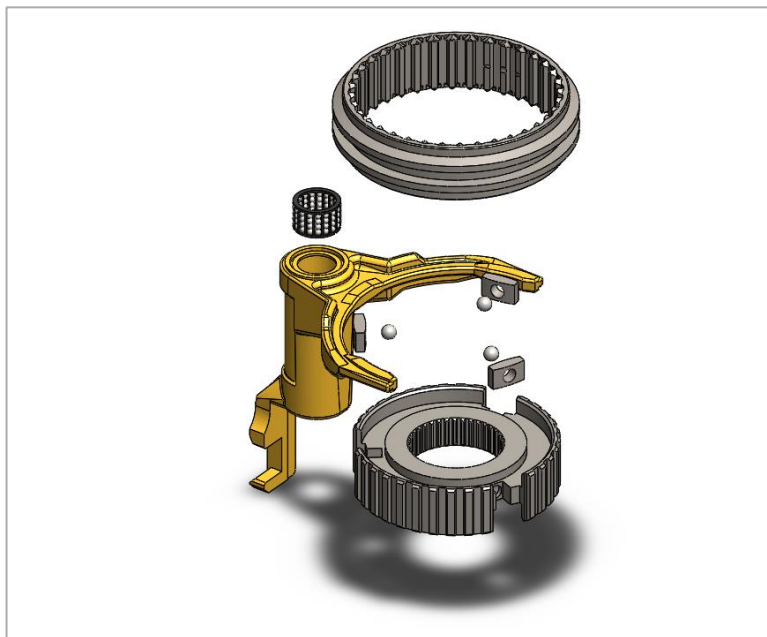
106 Explosionado buje y desplazable 1ª – 2ª
